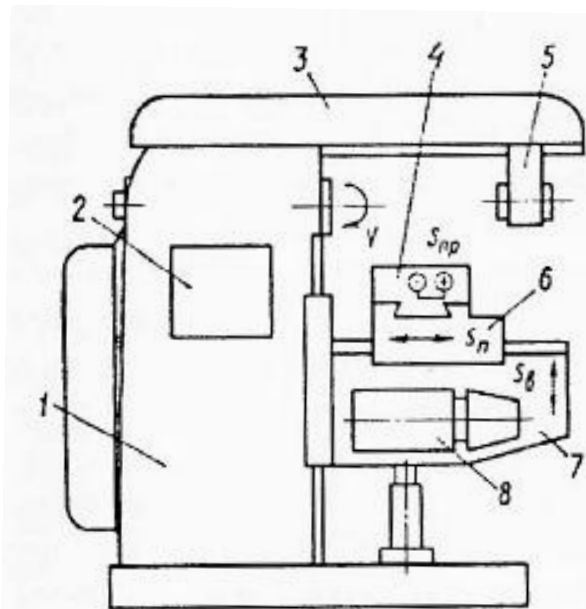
Горизонтально-фрезерувальний верстат
